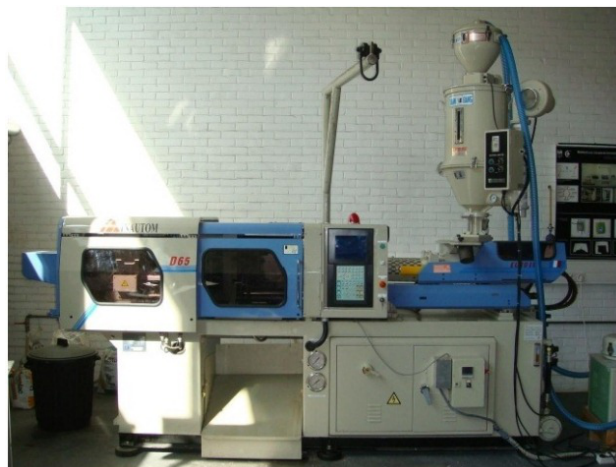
Máquina de moldação por injeção EURO INJ D065.
